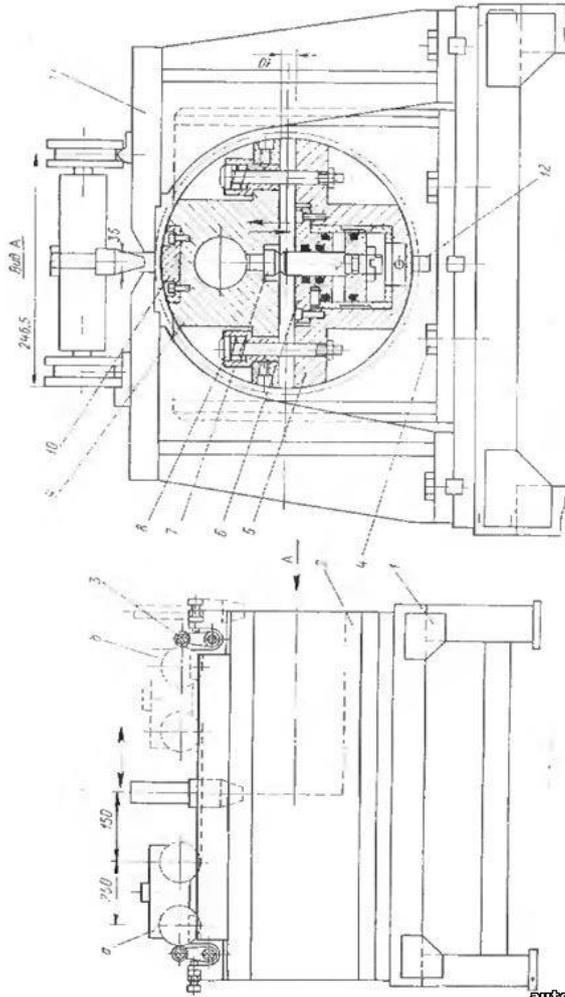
Приспособление для автоматической сварки продольного шва обечайки воздушного баллона трактора Т-150:
